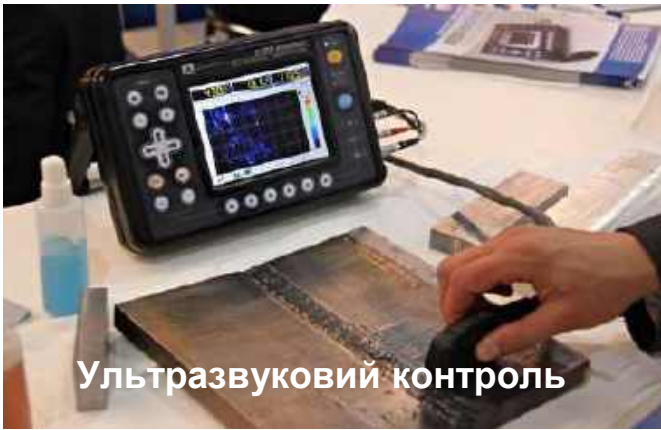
Неруйнівний контроль виготовлення зварних з'єднань
